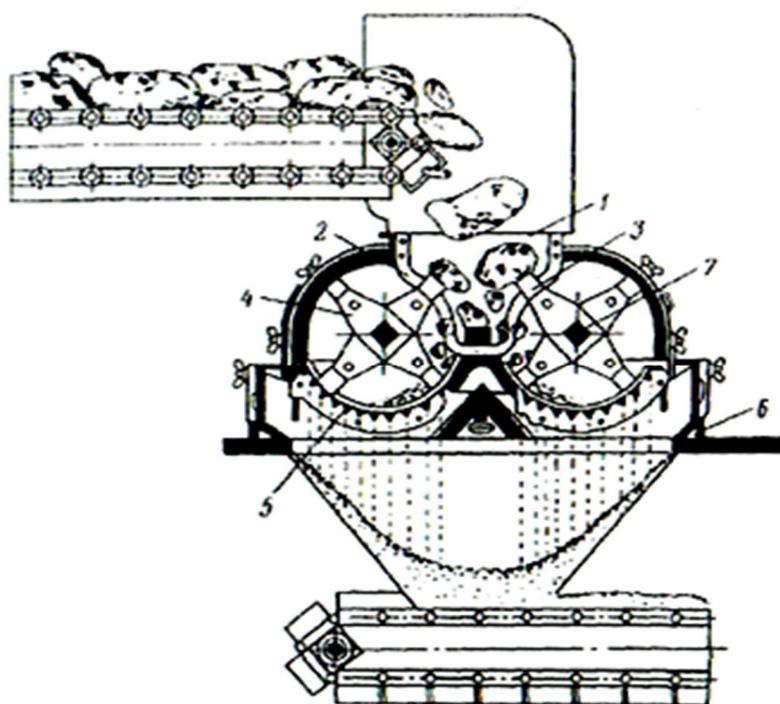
Молотковая двухроторная дробилка с параллельным расположением роторов: 1 — загрузочная воронка; 2 — фигурные колосники; 3 — молотки; 4 — держатели молотков; 5 — колосниковые решетки; 6 — корпус дробилки; 7 — роторные валы
